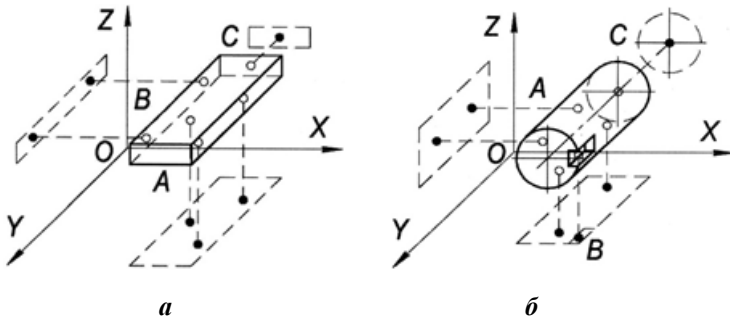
Базування призматичної (*а*) і циліндричної (*б*) деталей
